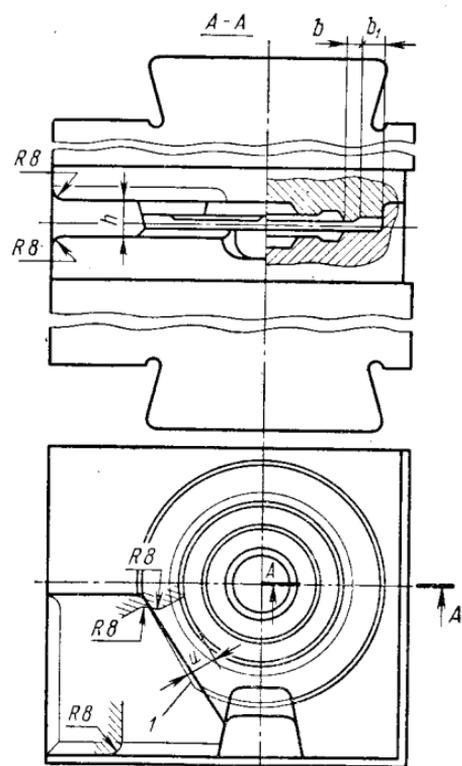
Штампы с площадкой для осадки при круглом замке:
